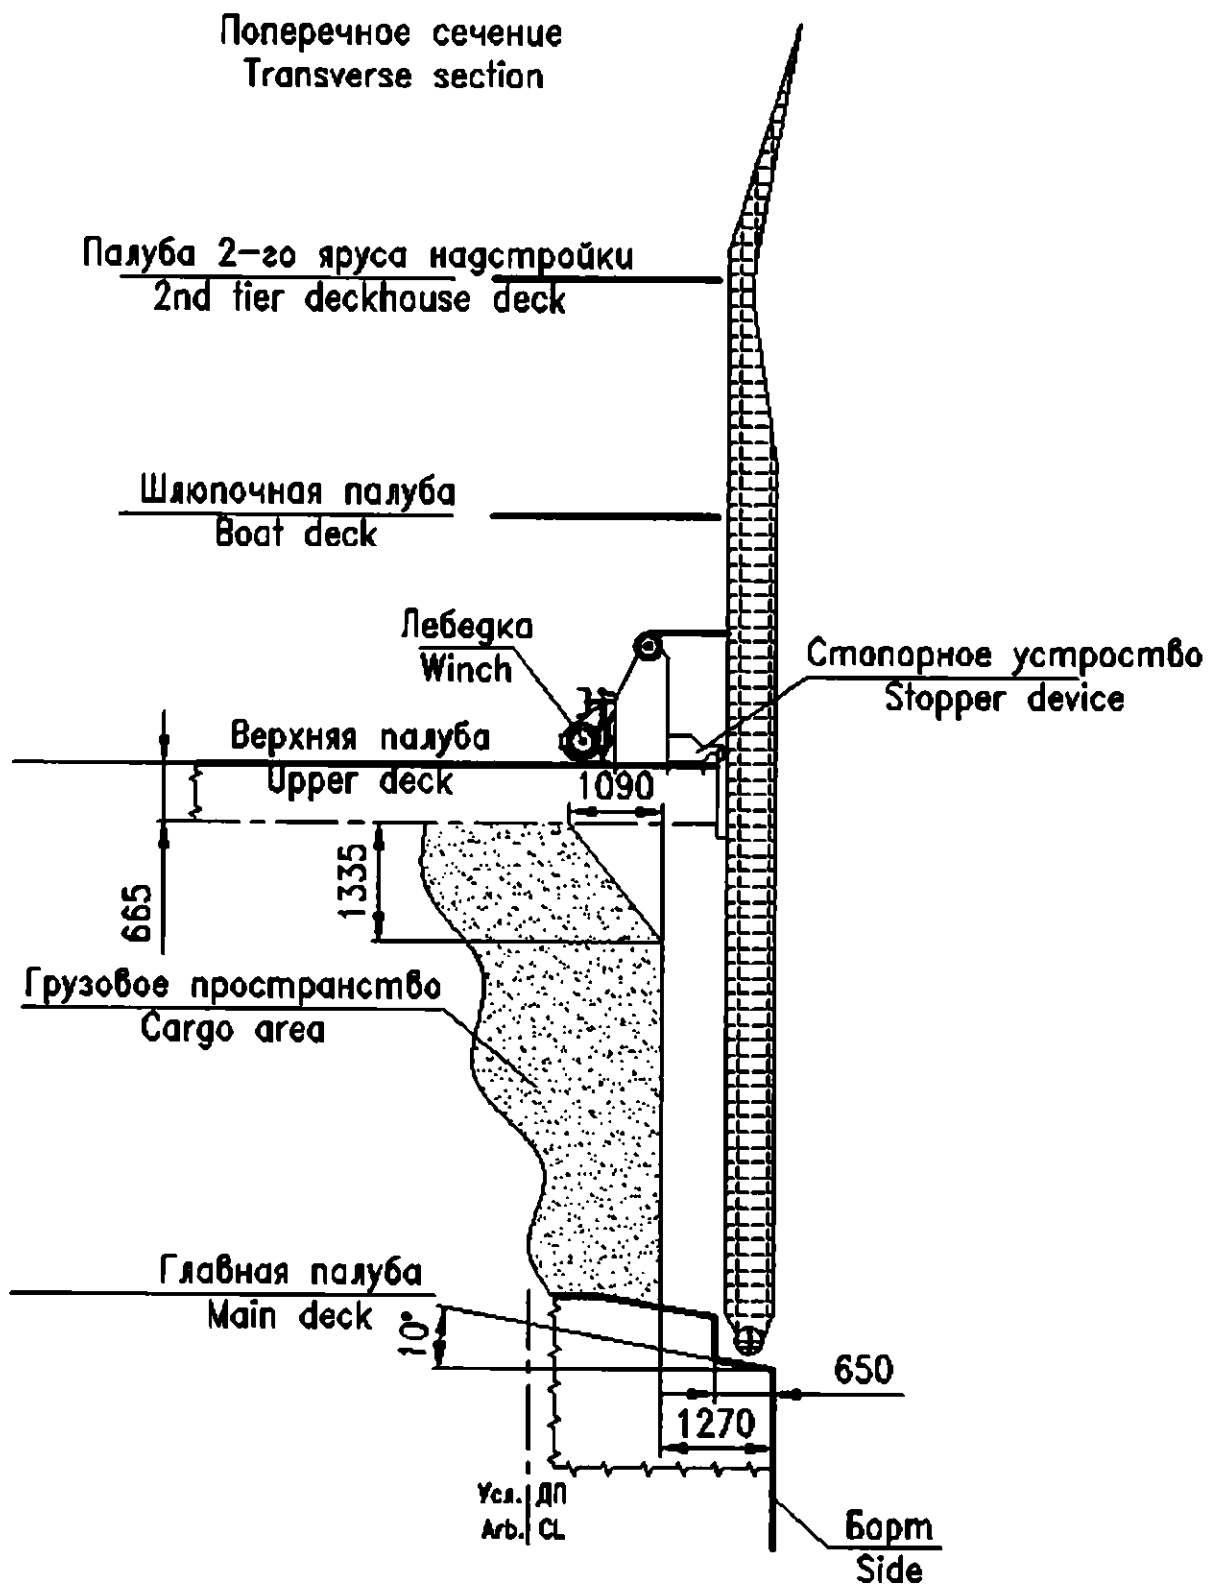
Габаритные размеры поперечный вид / Overall dimensions transverse view.
